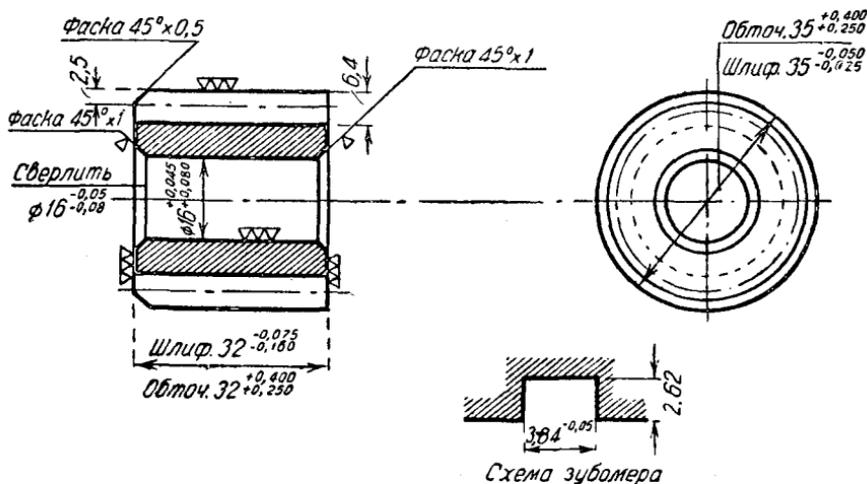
; Дет. 223; Внутренняя ведомая шестерня масляного насоса
